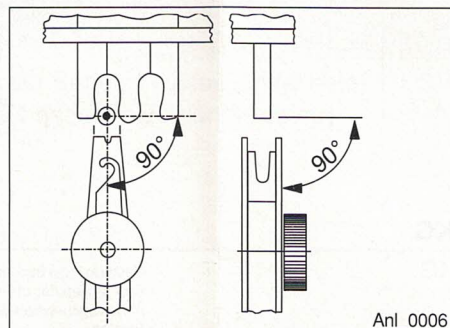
Anlegewerkzeug gerade anlegen / Fig. 6: Set termination tool straight
